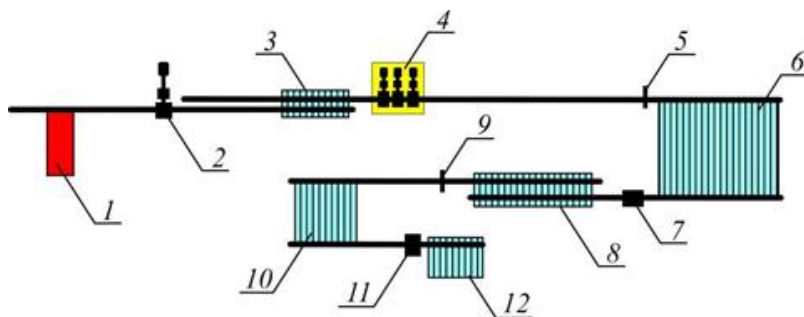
Крупносортный стан: 1 – нагревательная печь; 2 – обжимная клетка; 3 – поперечный транспортер; 4 – группа тандем; 5 – пила горячей резки; 6 – холодильник; 7 – роликовая правильная машина; 8 – собирающий транспортер; 9 – пила холодной резки; 10 – штабелирующая установка; 11 – обвязочная машина; 12 – разгрузочная решетка
